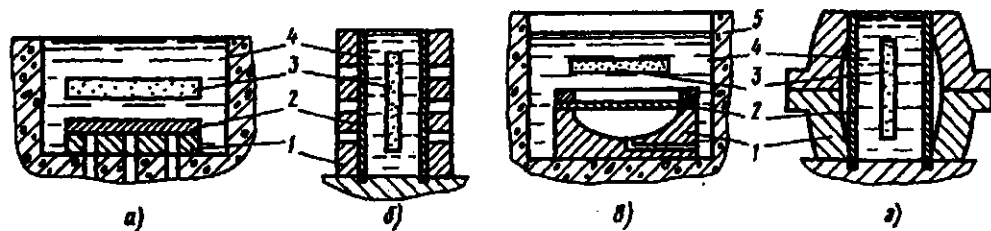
Схемы штамповки взрывом плоской и трубчатой заготовок: а — пробивка отверстий в листовой заготовке; б — пробивка отверстий в трубчатой заготовке; в — вытяжка полусферы из листовой заготовки; г — формовка-раздача трубчатой заготовки; 1 — матрица; 2 — заготовка; 3 — ВВ; 4 — передающая среда (вода); 5 — бассейн с рабочей средой
